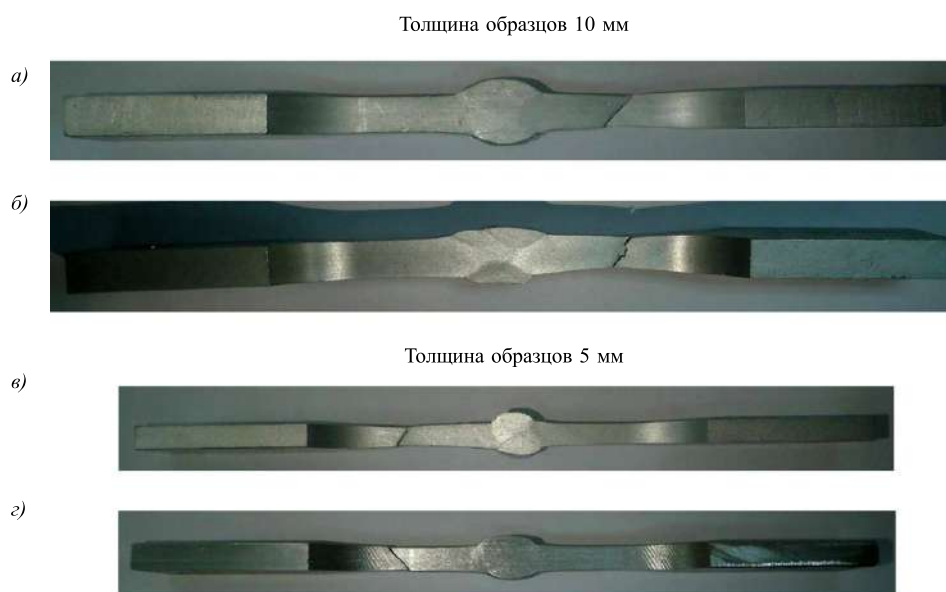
Характер разрушения сварных образцов с выпуклостью сварного шва сплавов 1550 (а, в) и 1565 (б, г), испытанных при температуре 293 К
